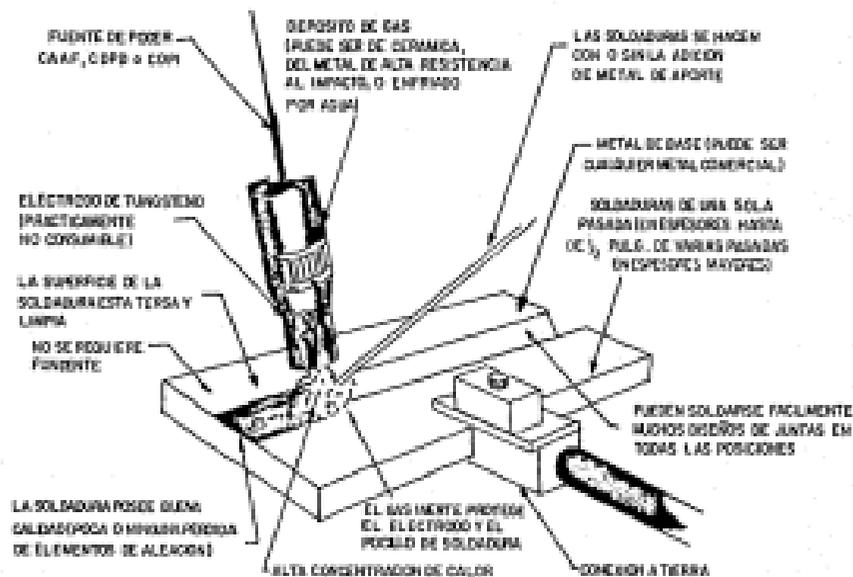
ELEMENTOS Y ASPECTOS ESENCIALES DEL PROCESO DE SOLDADURA TIG.
